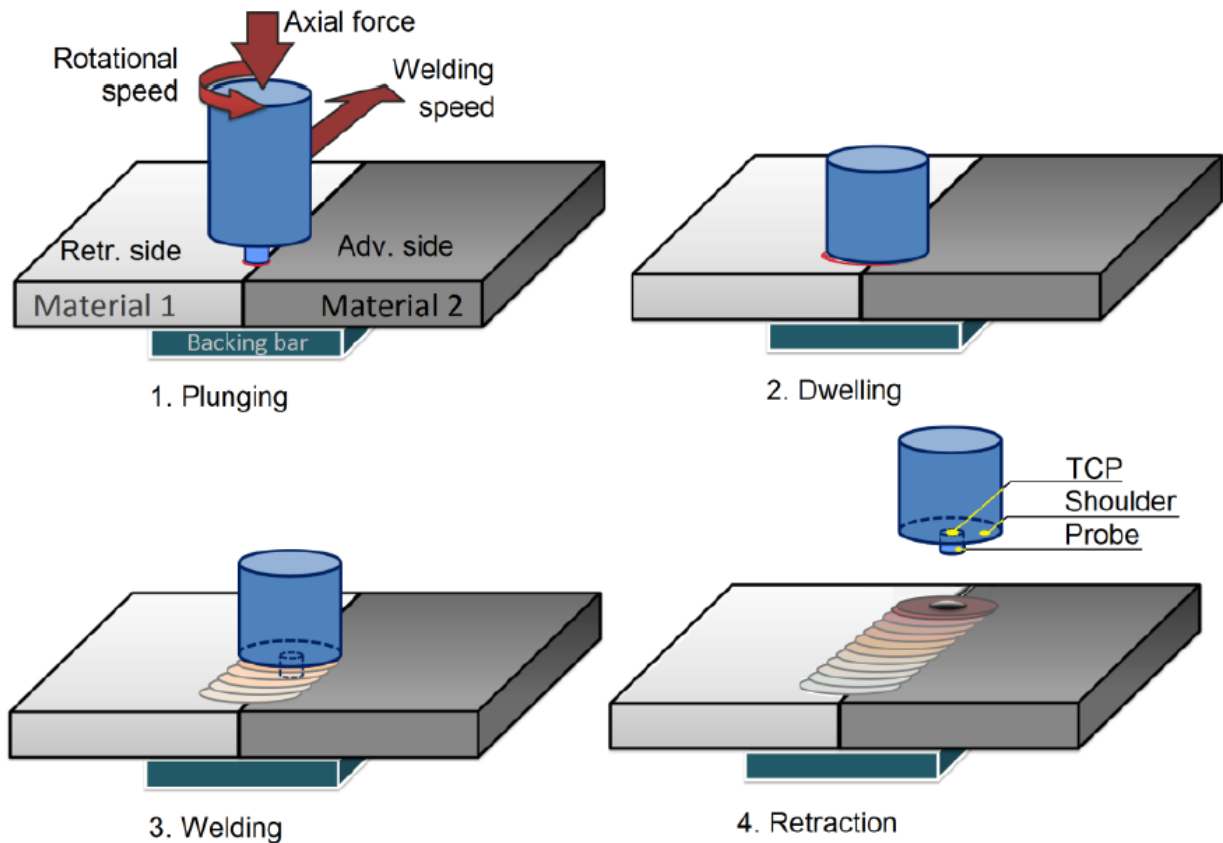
Componentes principais e direções de movimento envolvidos em FSW [4].
